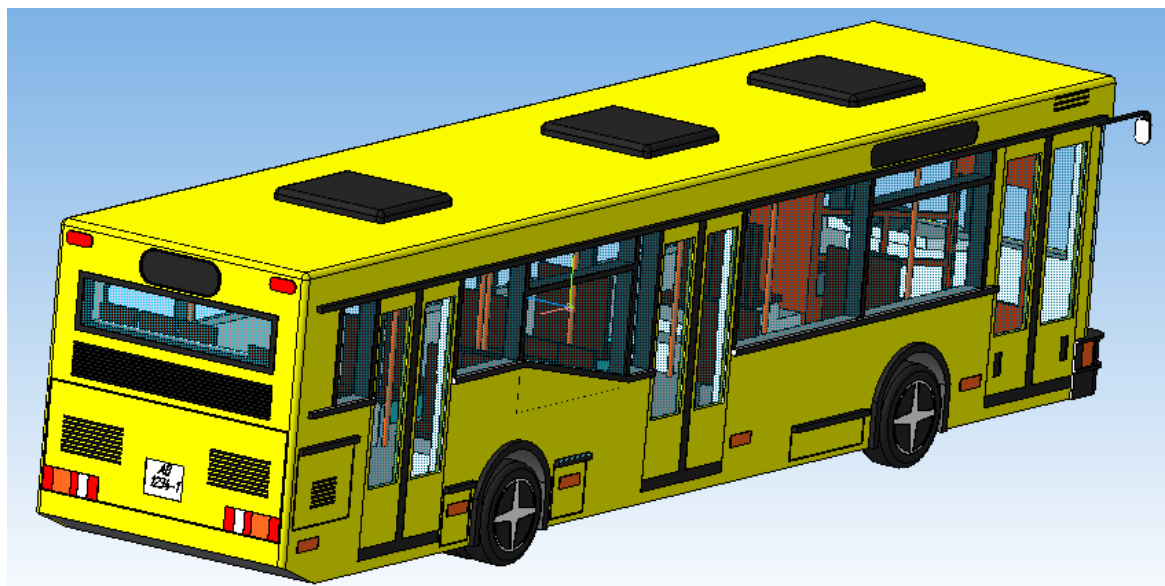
Основные размеры и планировка автобуса МАЗ 104
